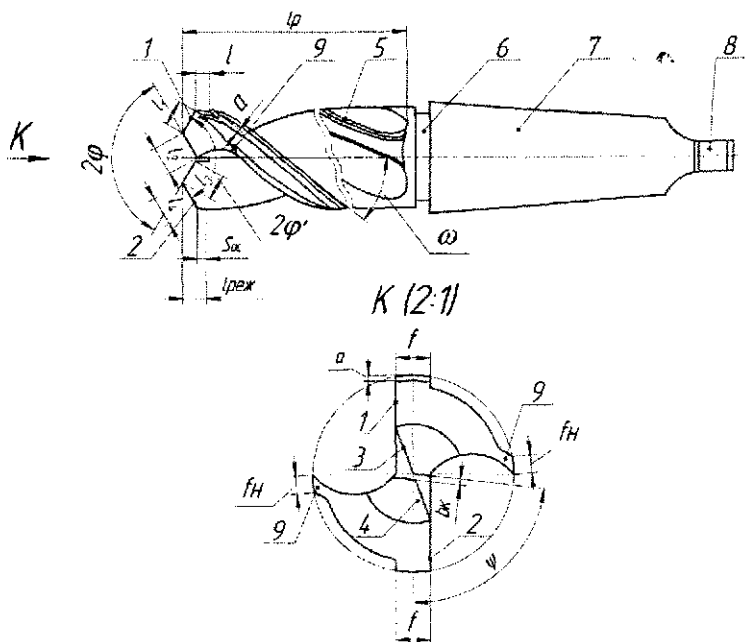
Двухвершинное спиральное сверло без поперечной кромки с подточкой ленточки
